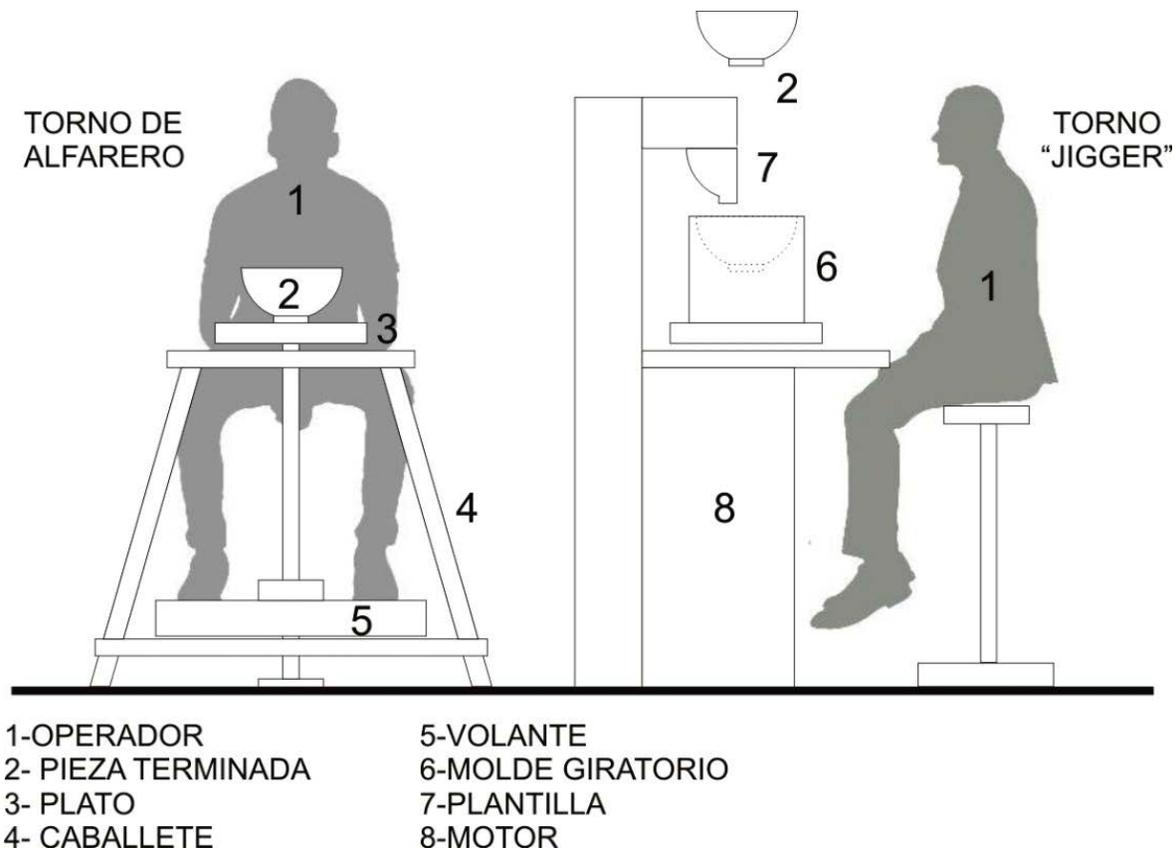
Torno de alfarero tradicional (izquierda) y jiggero de molde giratorio (derecha). Las operaciones *jigg and jolly* implicaban un torneado interior por plantilla y un moldeo externo por giro contra un molde. Elaborado por el autor en base a Langeweg (2004).
